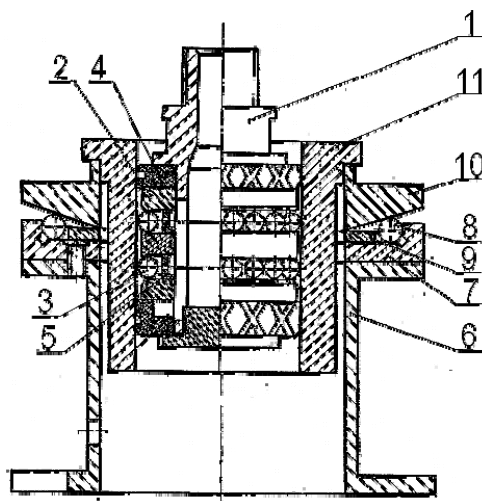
Пневмоцентробежный раскатник и устройство для обработки гильз цилиндров: 1 – корпус двухрядного шарикового раскатника; 2 – диски; 3 – деформирующие шары; 4 – центрирующие кольца; 5 – распорные втулки; 6 – сварной корпус приспособления; 7 – кольцо; 8 – шарики; 9 – сепаратор; 10 – диск; 11 – обрабатываемая гильза
